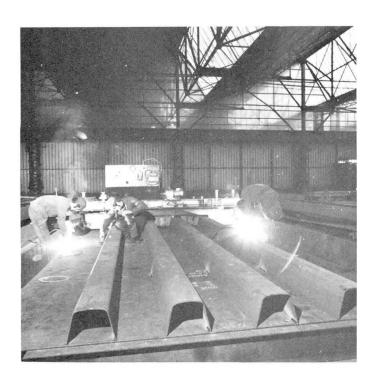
Portique de soudage des longerons de la dalle orthotrope
